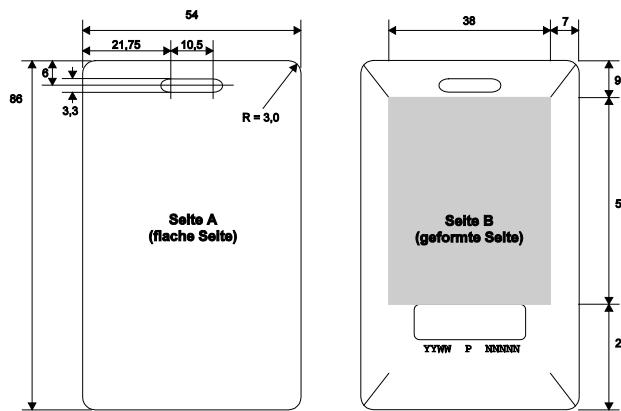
Dimensiones en mm: tarjeta EasyMove
